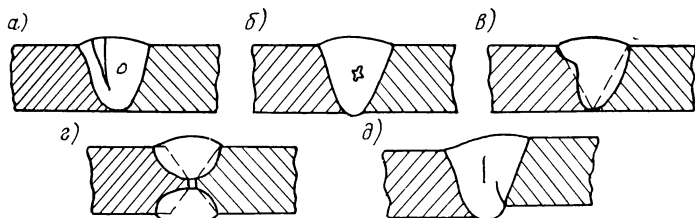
Внутренние дефекты сварных соединений: а — поры и свищи; б — твердые включения (шлак); в — несплавления; г — непровар; д — трещина.
